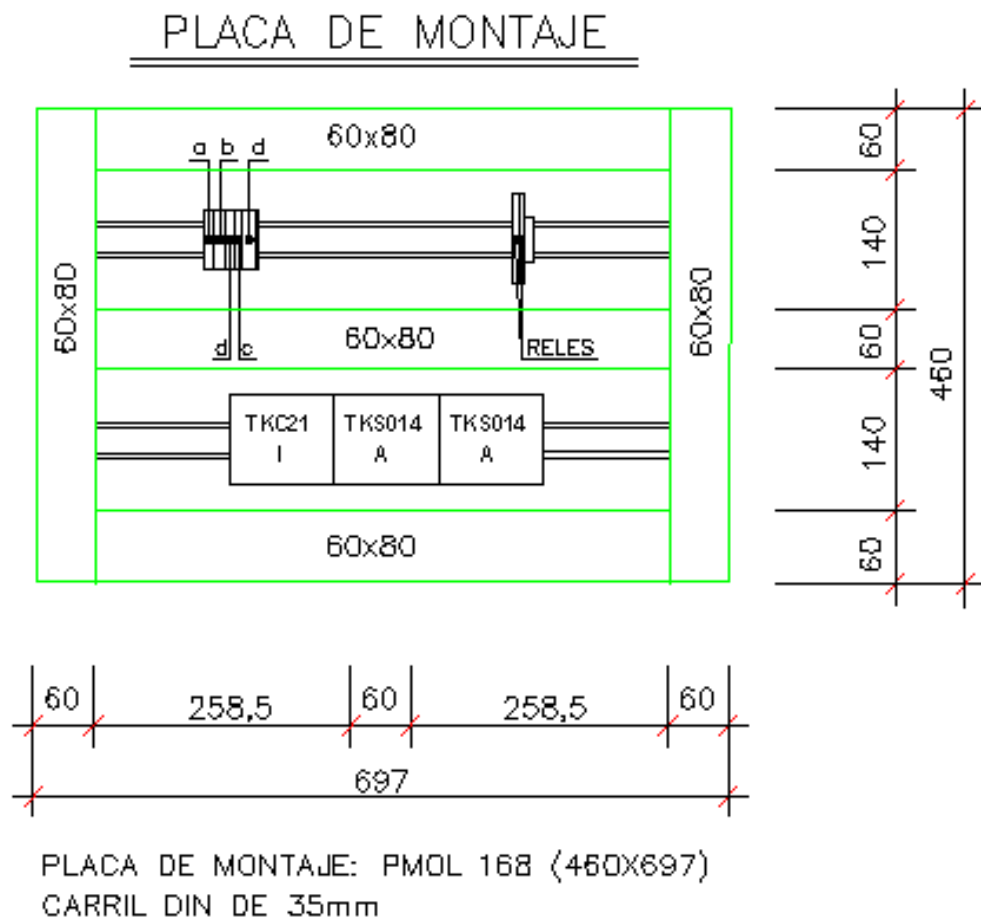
Diseño placas de montaje de equipos de seguridad en tornos
